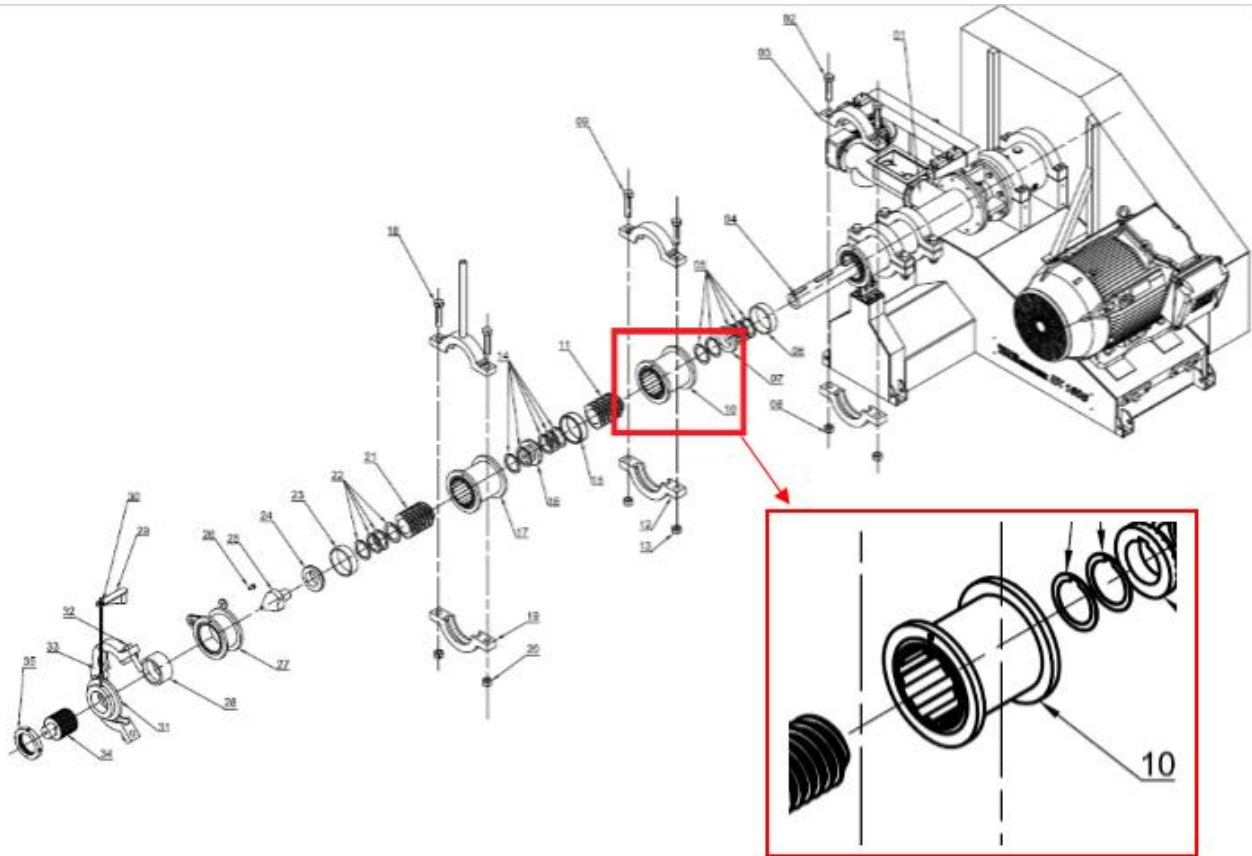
Despiece de extrusor de soja IMDB EX1605.
